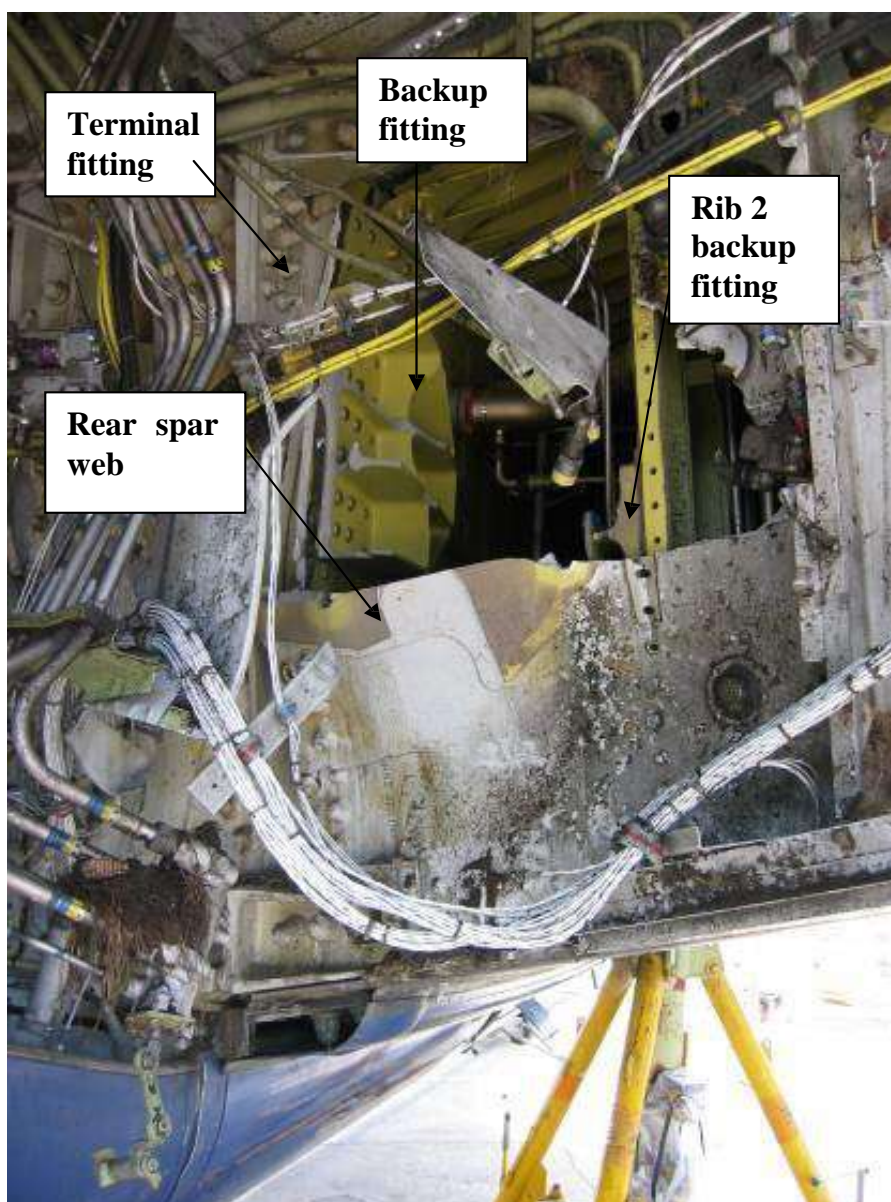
Внешний вид разрушения заднего лонжерона правой консоли крыла и топливного бака в месте крепления переднего подкоса ООШ
